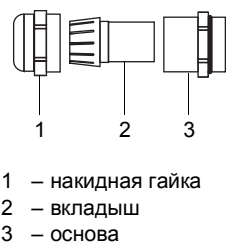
Кабельный сальник для корпуса из нержавеющей стали
